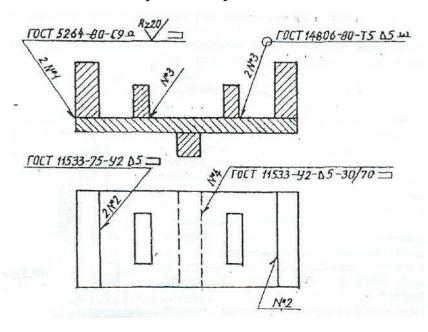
Условное обозначение сварных соединений
